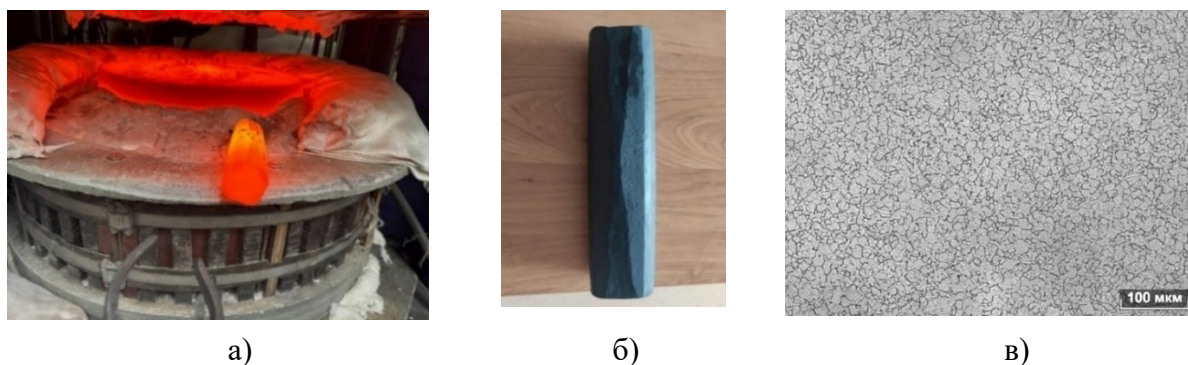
Процессковки слитка из сплава системы Co-Cr-Mo (а), внешний вид ковanej заготовки (б) и ее микроструктура (в)
